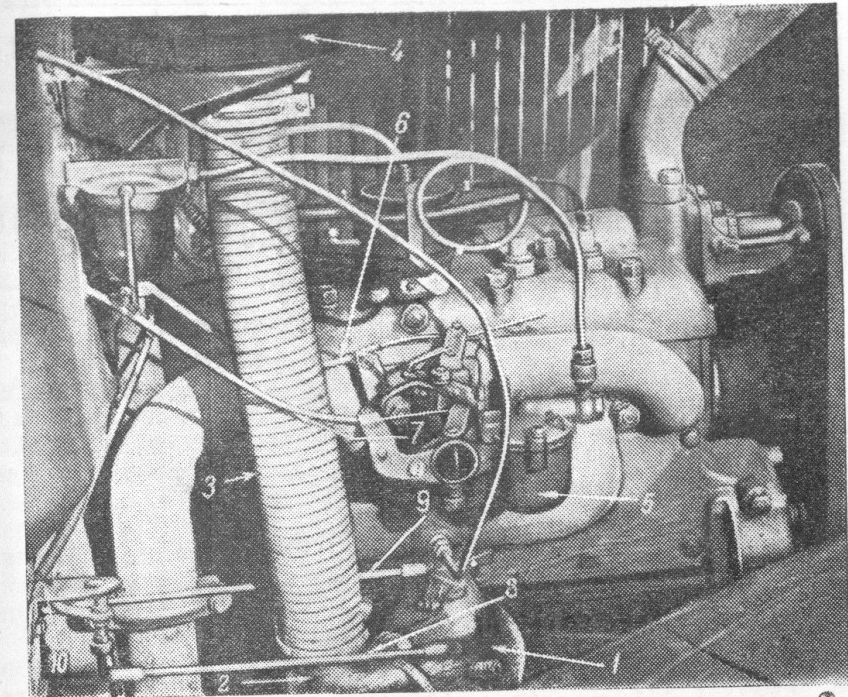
Двигатель ГАЗ-42 в сборе (вид со стороны системы питания):
